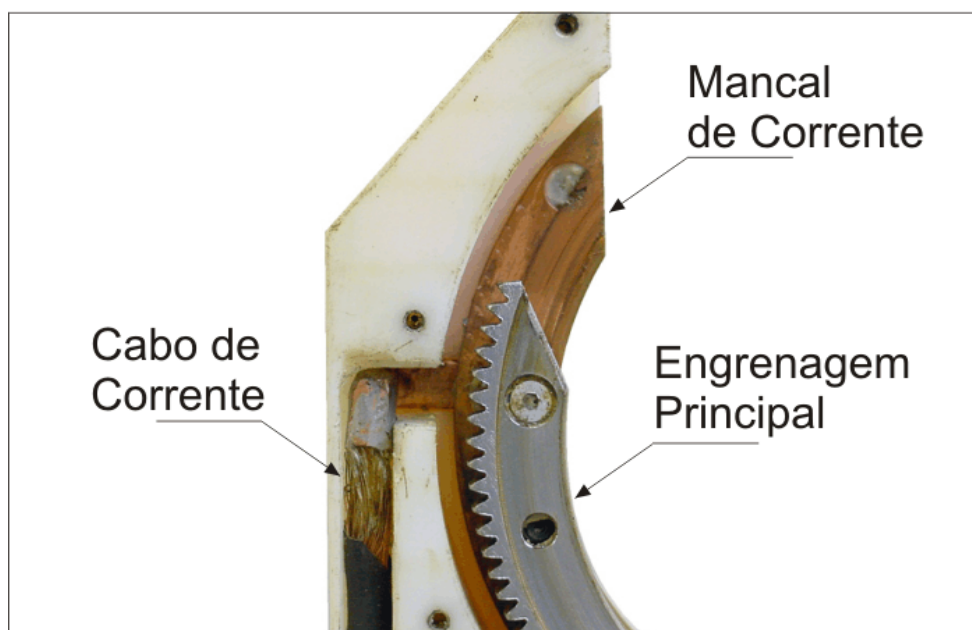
Contato elétrico entre o mancal e a engrenagem principal
